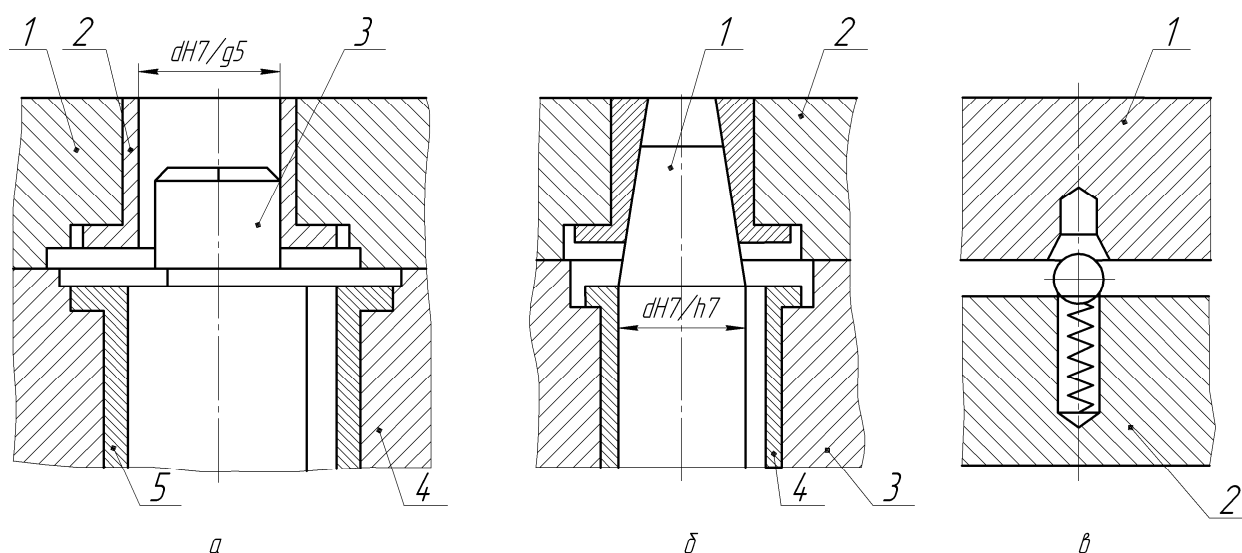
Різні типи фіксаторів ділільних пристроїв у розрізі: *a* – із циліндричним пальцем (1 – поворотна частина пристрою; 2, 5 – втулки; 3 – циліндричний фіксатор; 4 – корпус пристрою); *б* – з конічним пальцем (1 – конічний палець; 2 – поворотна частина пристрою; 3 – корпус пристрою; 4 – втулка); *в* – кульковий (1 – поворотна частина пристрою; 2 – корпус пристрою)
